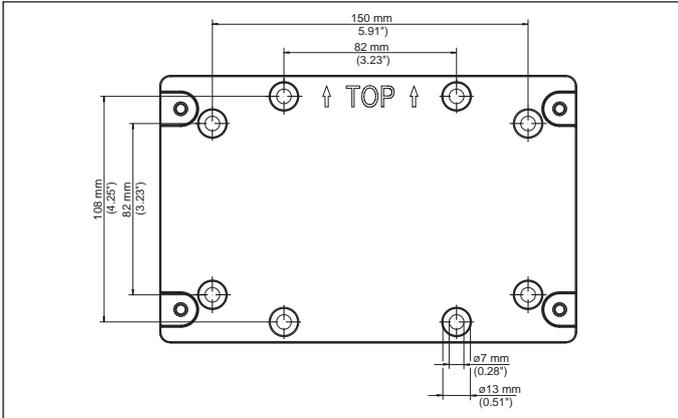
Plaque de montage pour montage mural (VEGAMET 861, 862)
